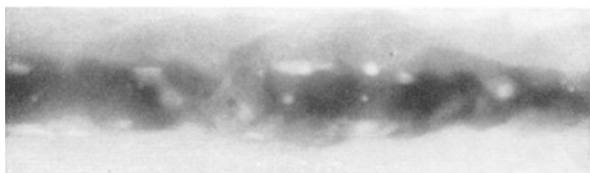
Röntgenaufnahme einer schlechten Elektroschweißung.
